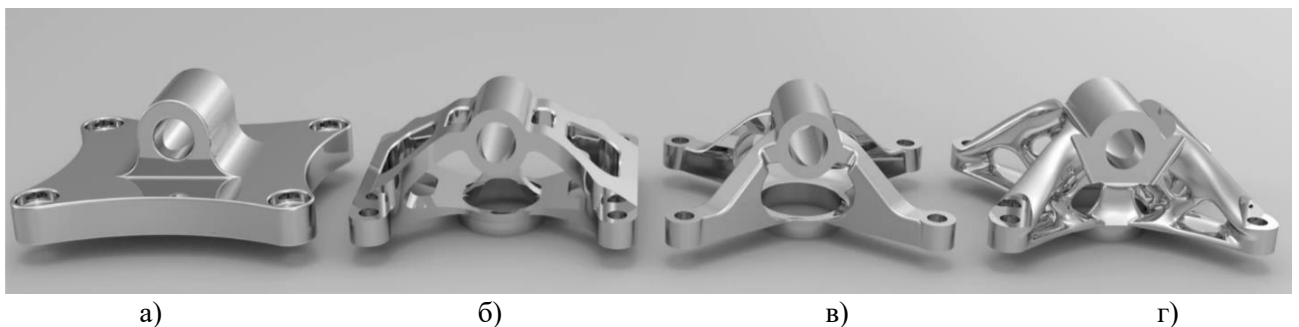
Зовнішній вигляд типової та згенерованих деталей:
